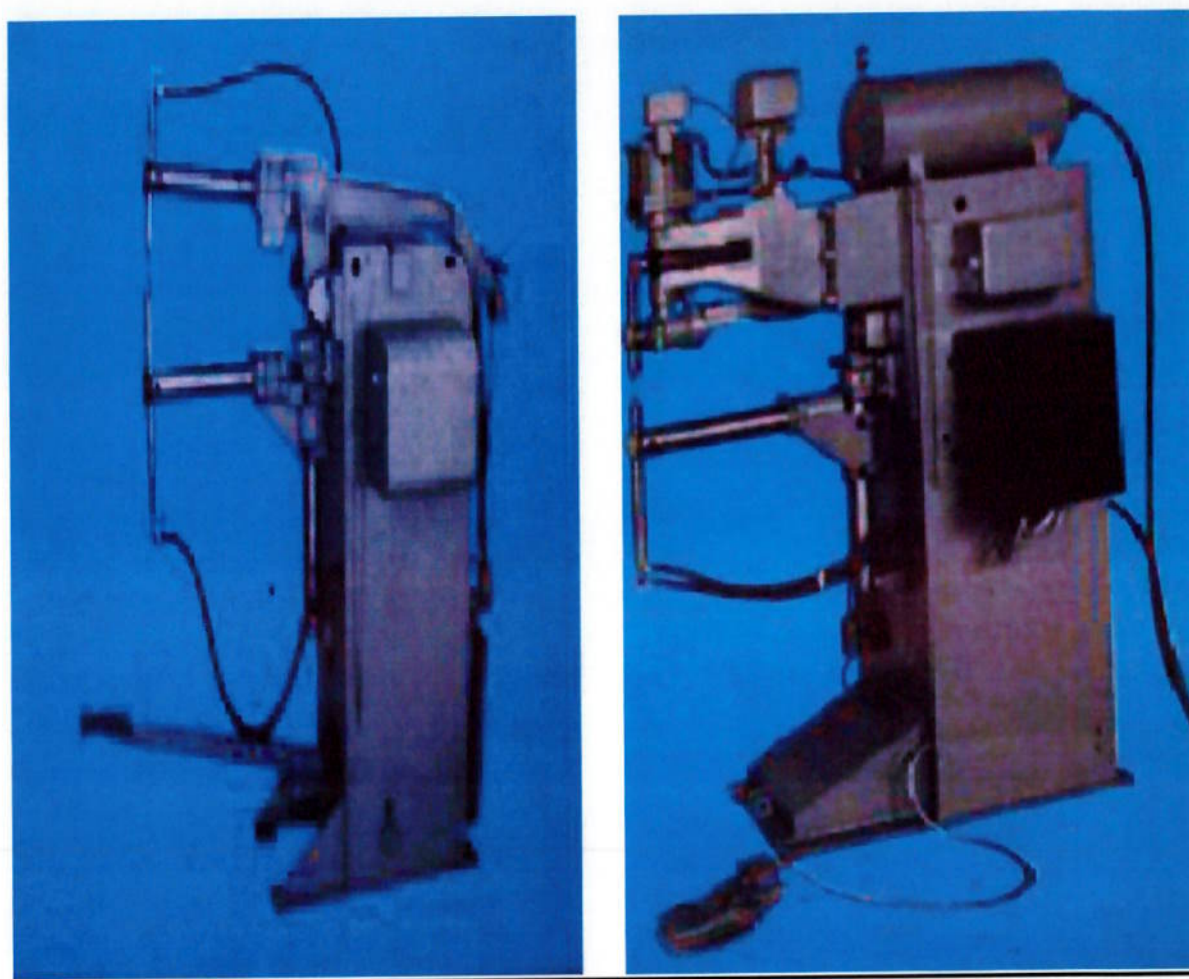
Máquinas de soldagem por resistência (Ponteadeira) [28].
